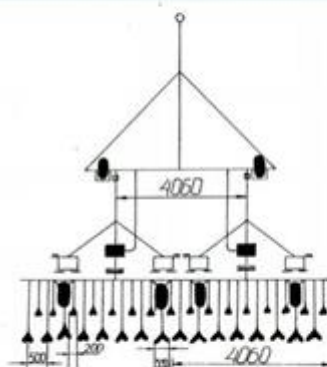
Схема расстановки рядов и стрельчатых лап КПС-4.
